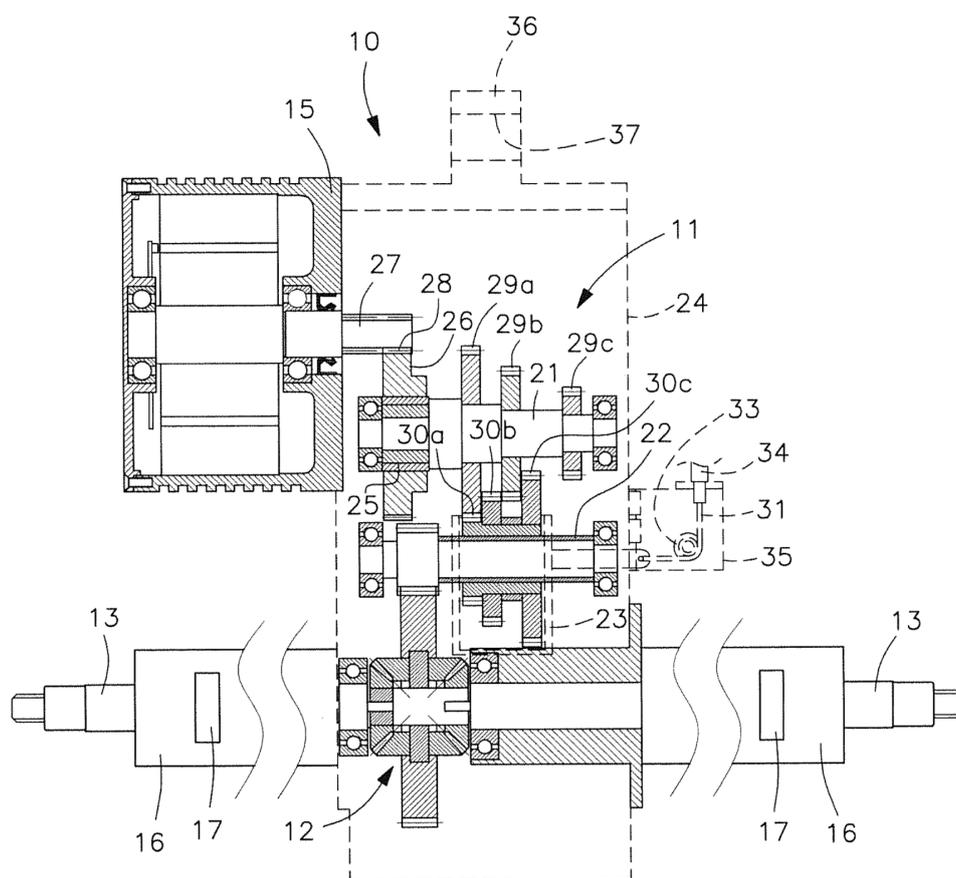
Схема трансмиссии с цилиндрическим трехступенчатым редуктором
